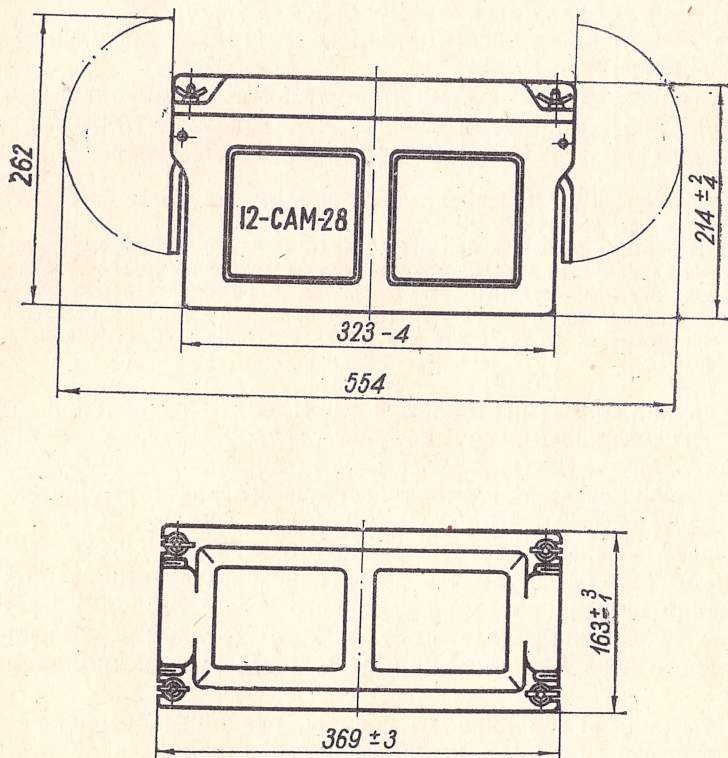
Габаритный чертеж аккумуляторной батареи 12-CAM-28
